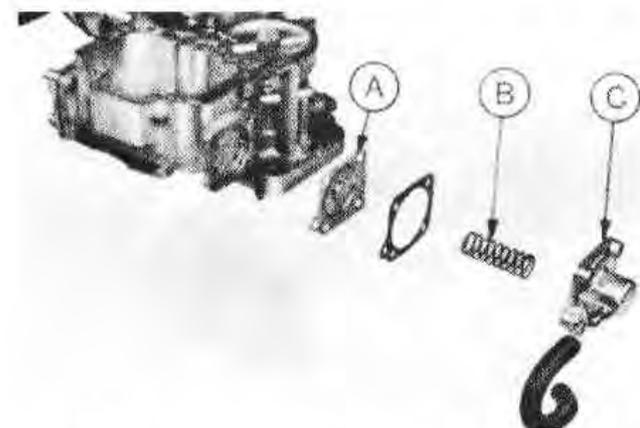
Диафрагма противоостановочного устройства (А), возвратная пружина (В) и корпус (С) (Разд.26)
